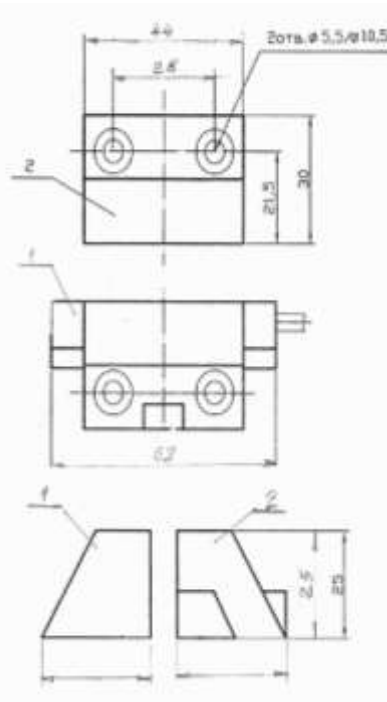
Извещатель охранной точечный магнитоконтактный «Барьер 2». Габаритные и присоединительные размеры.
